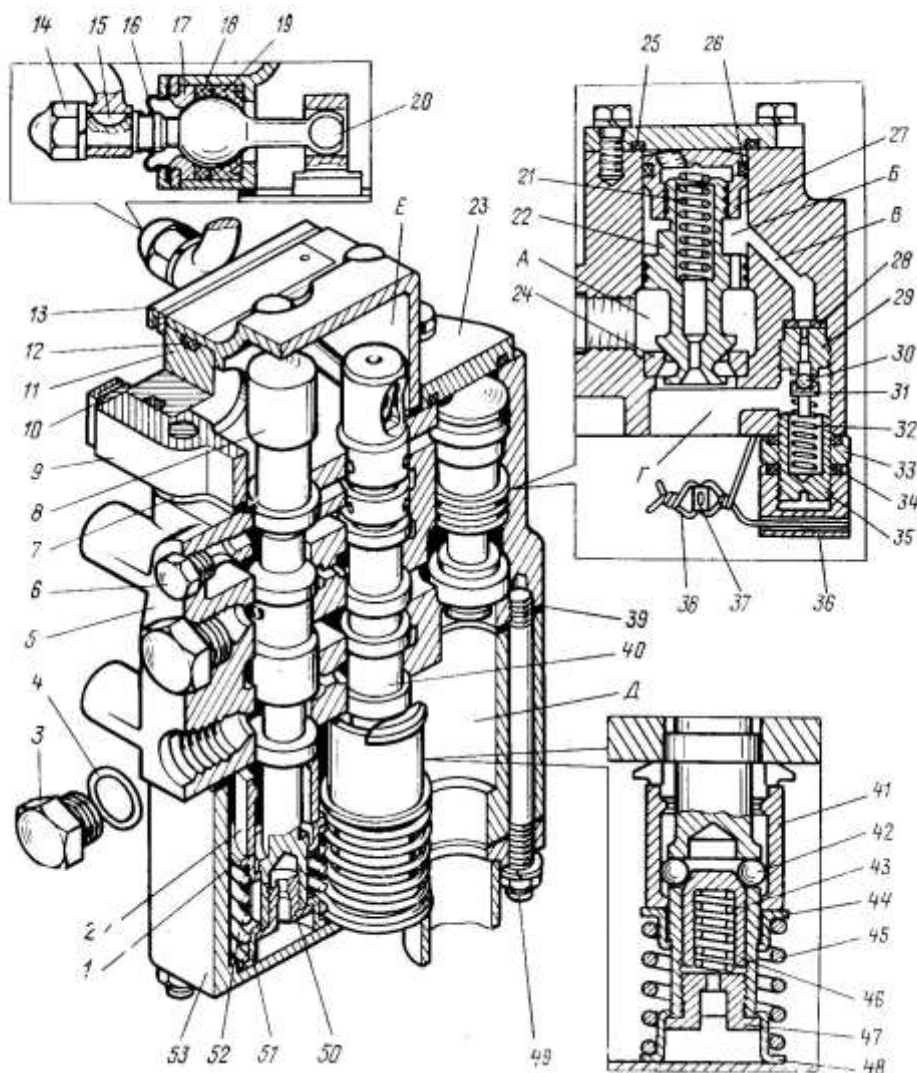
Распределитель: 1, 44 – верхние стаканы; 2 – обойма; 3 – заглушки; 4, 12, 18, 19, 25, 26, 34 – кольца уплотнительные; 5 – корпус; 6 – пробка; 7 – прокладка верхняя; 8 – перегрузочный клапан; 9 – крышка верхняя; 10 – пластина; 11 – втулка; 13 – накладка; 14 – колпачок; 15 – шпонка; 16 – пыльник; 17 – кольцо; 20 – рычаг; 21, 32, 43, 45, 52 – пружины; 22 – перепускной клапан; 23 – упор; 24 – гнездо клапана; 27 – направляющая перепускного клапана; 28 – прокладка; 29 – гнездо предохранительного клапана; 30, 42 – шарики; 31 – направляющая предохранительного клапана; 33 – гайка; 35 – винт регулировочный; 36-колпачок; 37 – пломба; 38 – проволока; 39 – прокладка нижняя; 40 – золотник; 41 – обойма фиксатора; 46 – втулка конусная; 47, 50 – пробки; 48, 51 – стаканы нижние; 49 – шпилька; 53 – крышка нижняя
